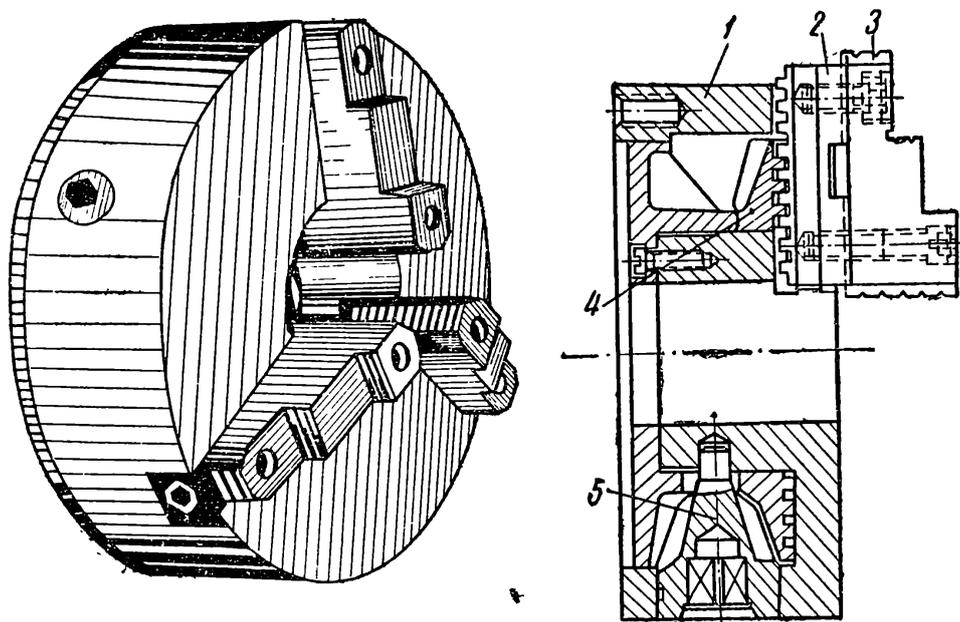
Трехкулачковый самоцентрирующий патрон:
